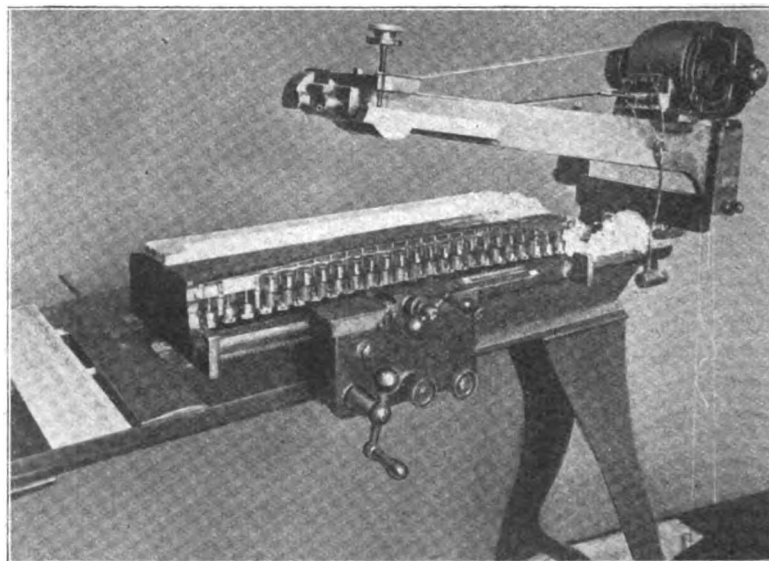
Schneidmaschine zum Ausschneiden von Holzflügeln mit veränderlichem Profil. Vor dem Werkstück liegt die als Leitkurve dienende Blattfeder mit den Mikrometerschrauben. Rahmen mit Schneidwerkzeug hochgeklappt.
